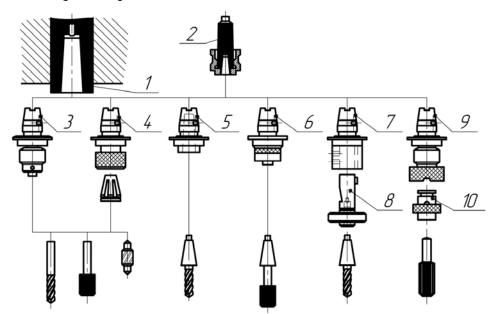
Инструментальная быстросменная система для сверлильных станков с ЧПУ: 1 — шпиндель станка; 2 — быстросменный патрон (базовый) с шариковым захватом; 3 — сверлильный патрон; 4 — цанговый патрон; 5 — вставка с внутренними конусами Морзе; 6 — плавающий патрон для разверток; 7 — вставка с цилиндрическим отверстием и пазом под шпонку; 8 — регулируемая цилиндрическая втулка; 9 — патрон для метчиков; 10 — быстросменная вставка
